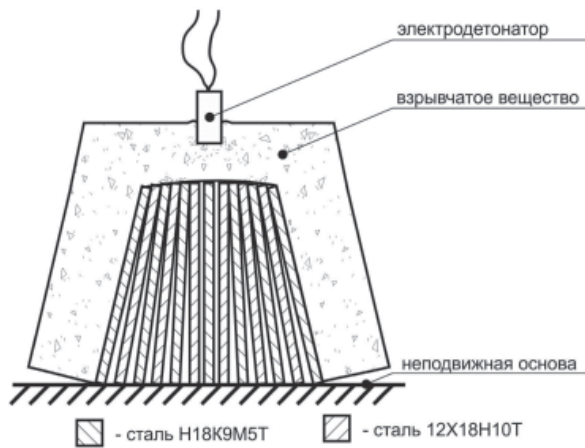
Схема сварки взрывом стальных пластин
